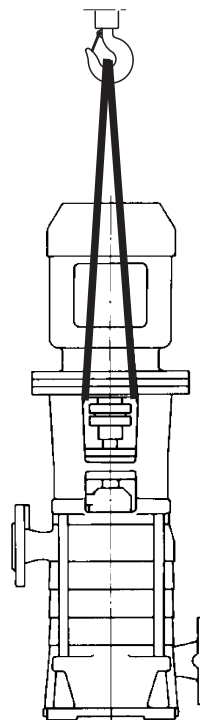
Hebezeug befestigen an vertikalem Pumpenaggregat
